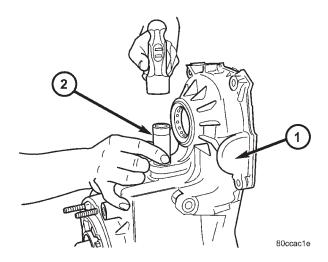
Desmontaje del cojinete del eje de sector de cambio
